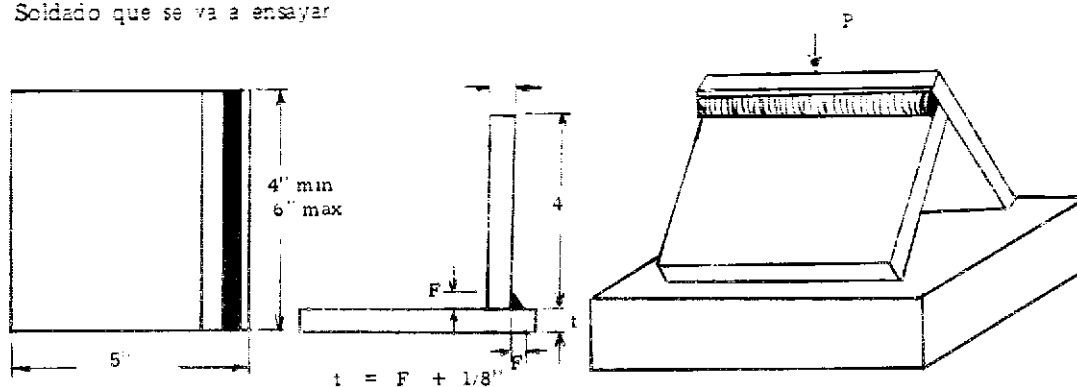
Especimen usado en el ensayo de fractura.
